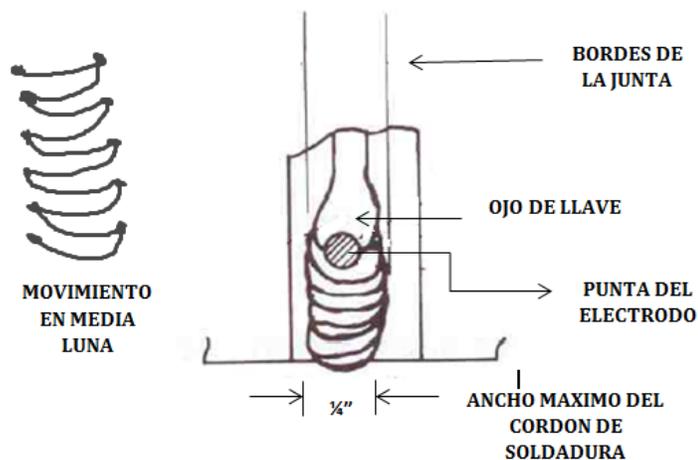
OJO DE LLAVE. PRIMER CORDÓN DE SOLDADURA.
